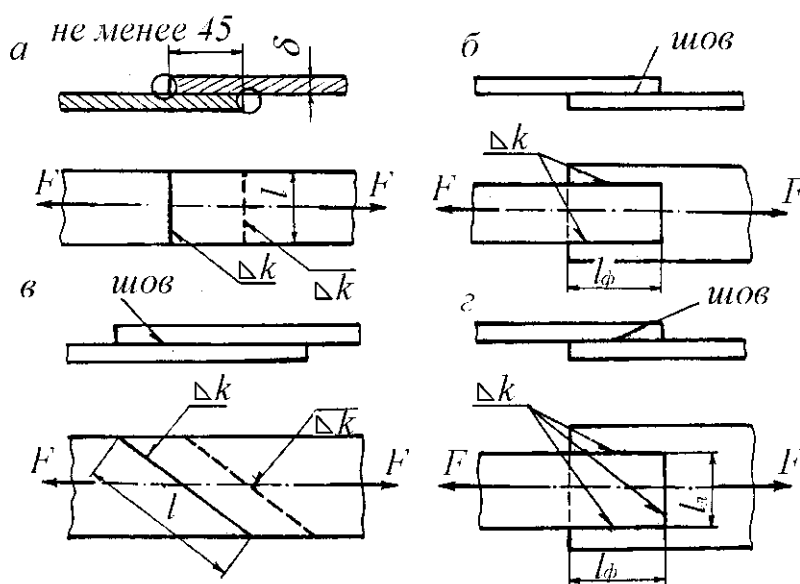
Соединения внахлестку угловыми сварными швами
